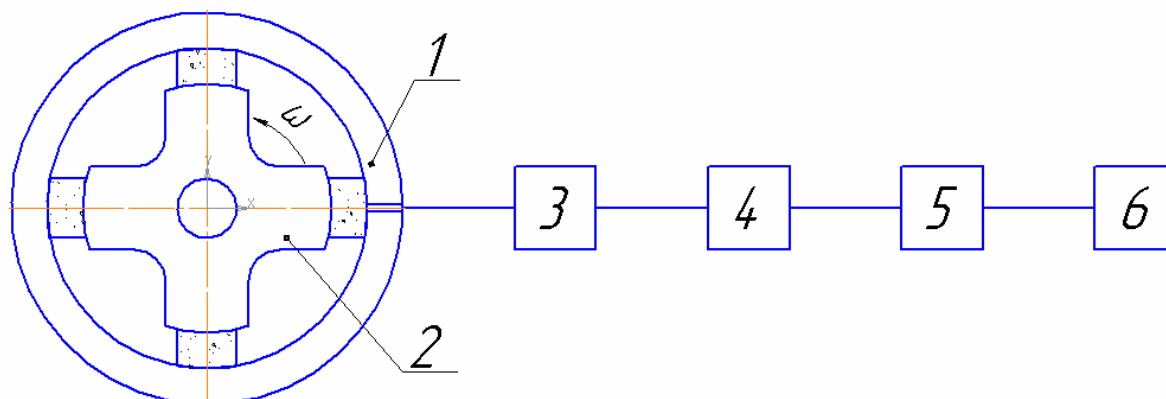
Схема для измерения температуры в зоне резания при обработке соосным шлифовальным инструментом (1 – заготовка; 2 – соосный шлифовальный инструмент; 3 – приемник инфракрасного излучения; 4 – усилитель; 5 – регистрирующий прибор; 6 – ПК)
